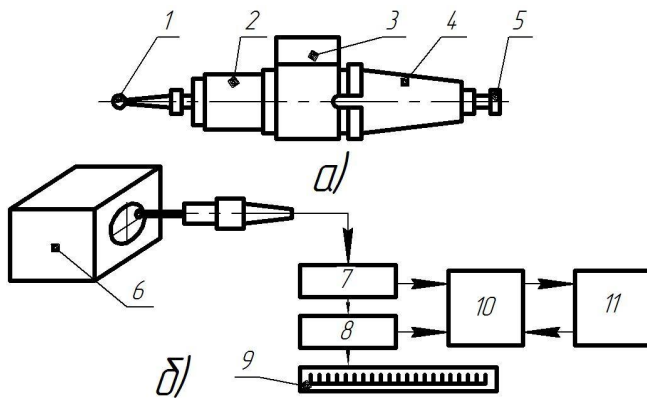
Пристрій автоматичного контролю на верстаті: а – датчик (1 – щуп; 2 – корпус; 3 – пристрій сигналізації; 4 – оправка; 5 – хвостовик); б – схема системи контролю (7 – пристрій пошуку сигналу; 8 – лічильник; 9 – пристрій зворотного зв'язку; 10 – пристрій контролю; 11 – пристрій ЧПК
